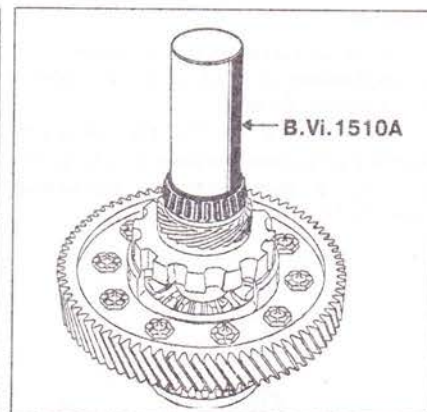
Установите малый подшипник при помощи приспособления В. Vi. 1510А.
